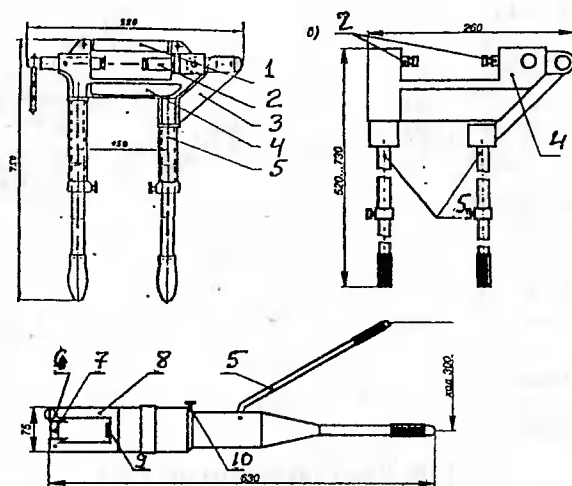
Пресс-ножницы ручные ПР-12 (а); пресс ПР-6 (б); пресс ПГР-20М (в): 1 — переключатель; 2 — плунжер; 3 — рычаг; 4 — корпус; 5 — ручка; 6 — ось; 7 — планка; 8 — вилка; 9 — регулировочный винт; 10 — вентиль
